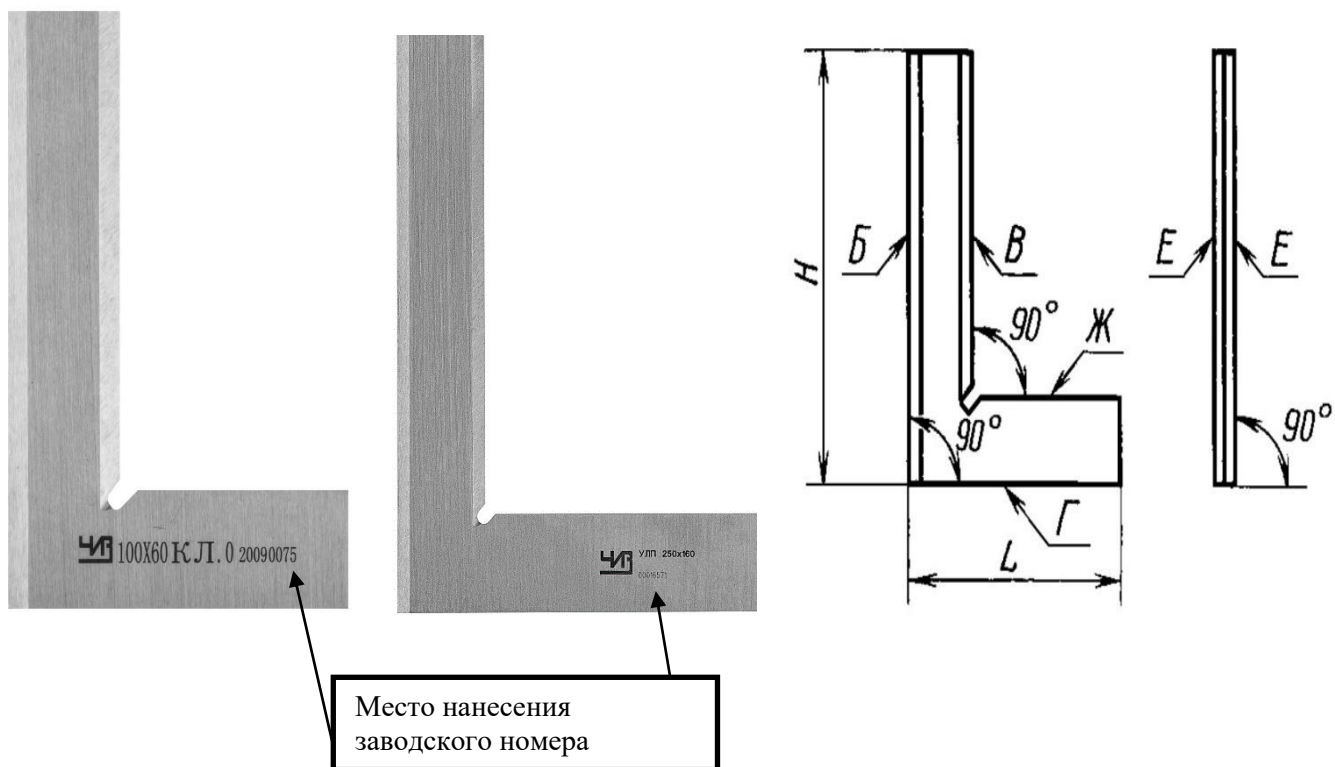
Общий вид угольников типа УЛП с местом нанесения заводского номера и обозначение условных размеров и поверхностей
